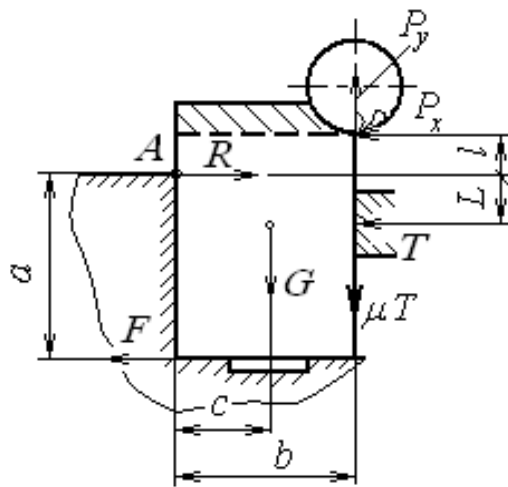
Сили, які діють на заготовку при фрезеруванні
